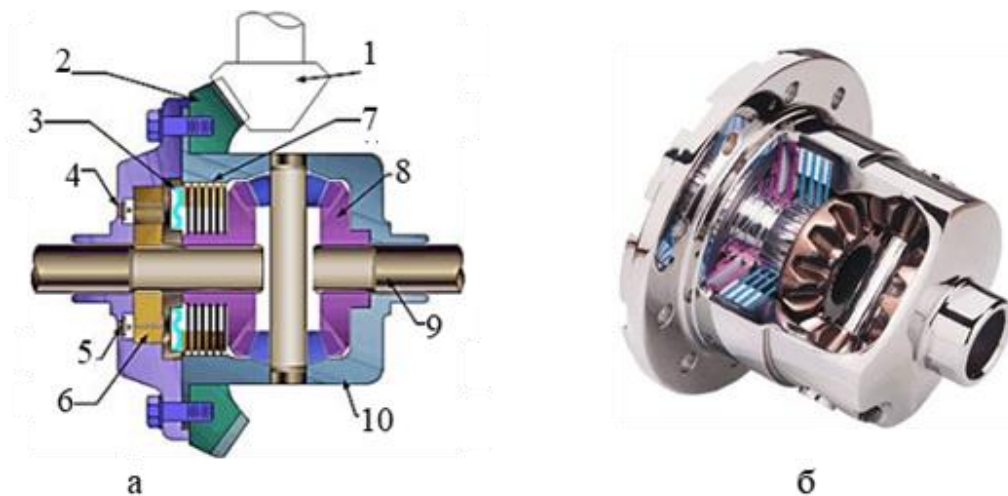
Героторний диференціал: а – устрій; б – зовнішній вигляд
